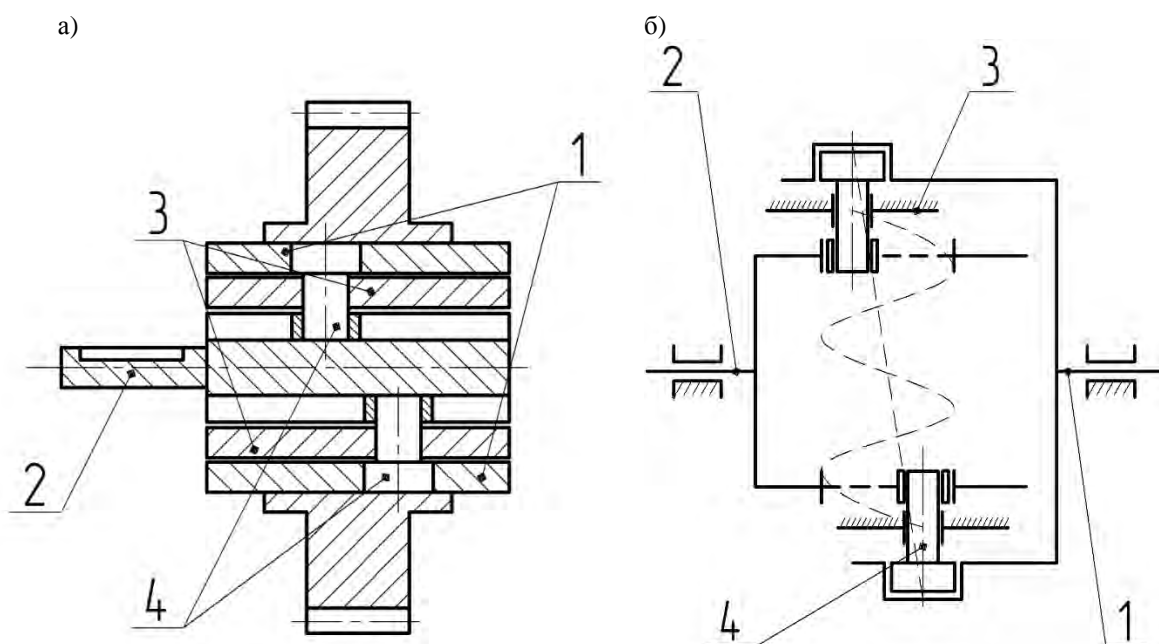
Передача с промежуточными телами качения с двухэлементными составными роликами: а – конструктивное исполнение; б – кинематическая схема
